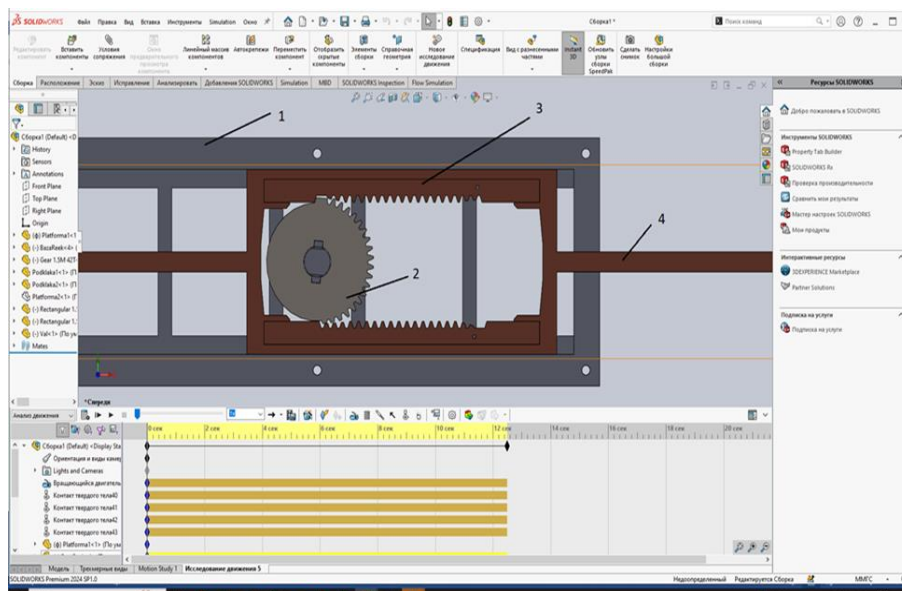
Чертеж поршневой установки, в программе SolidWorks где: 1- корпус, 2- вращающаяся шестерня на валу, 3- линейная шестерня, 4 -шток поршня (шатунь поршня)
